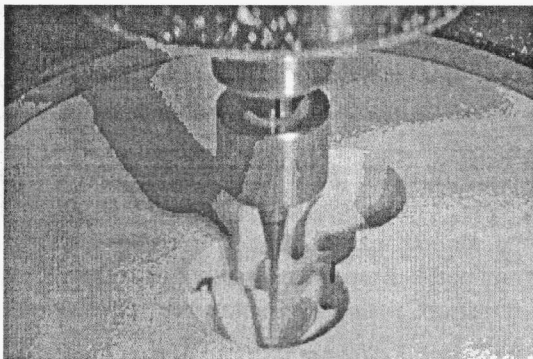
Виготовлення ортопедичних конструкцій за допомогою фрезувального апарата
